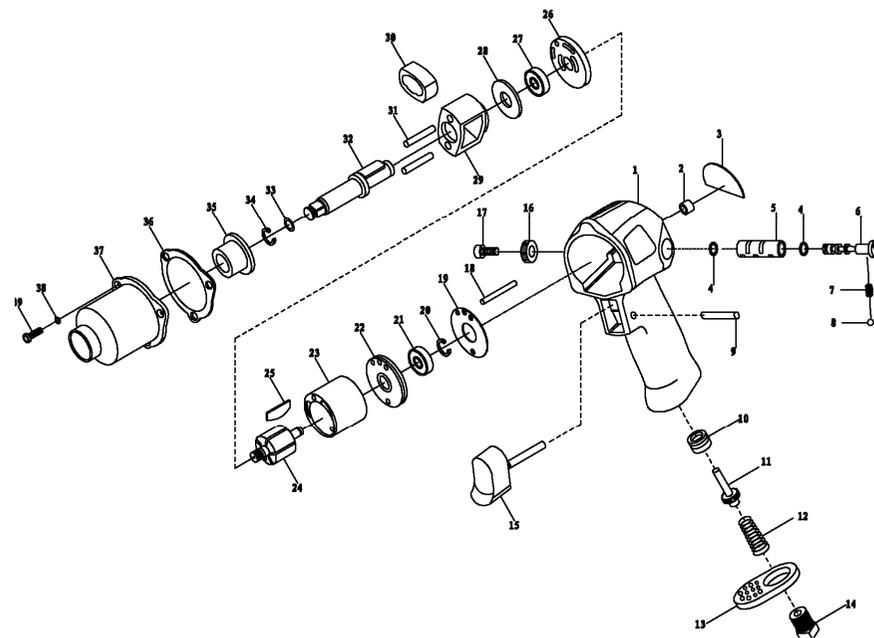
Схема устройства и сборки гайковерта ручного пневматического MFV 014/312-1.
